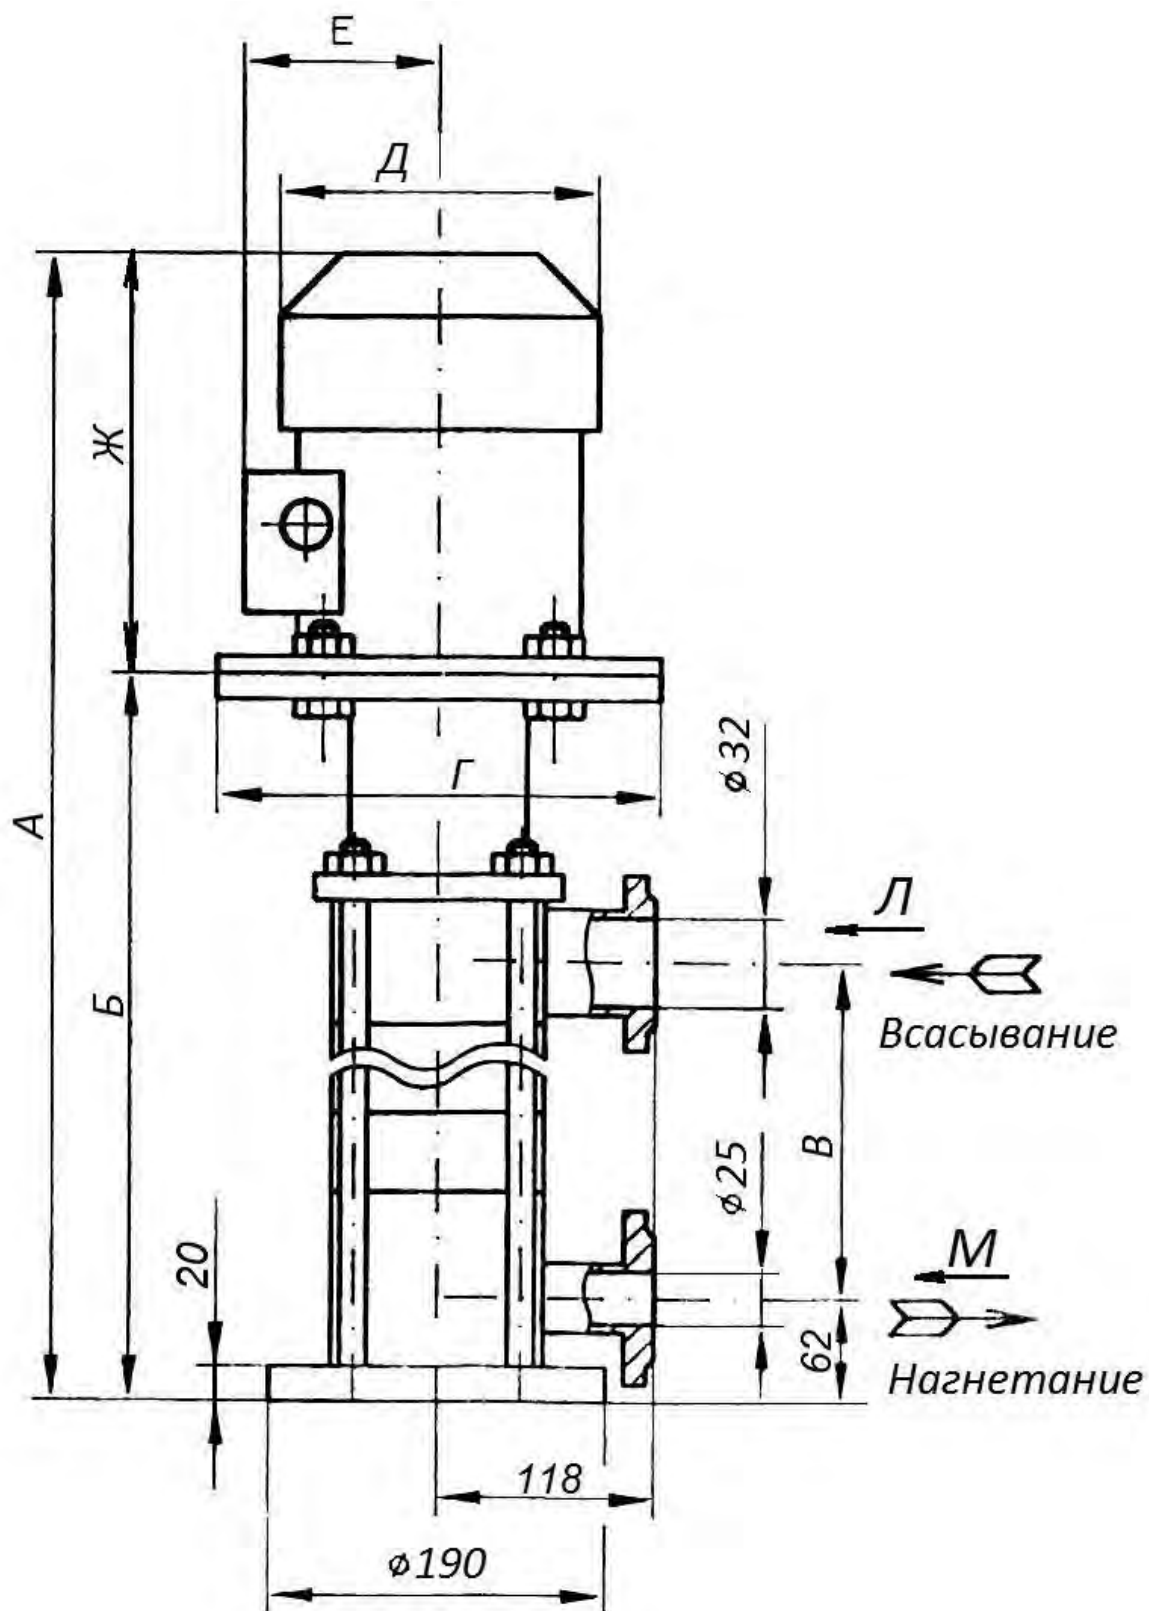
Общий вид насоса с габаритными и установочными размерами
